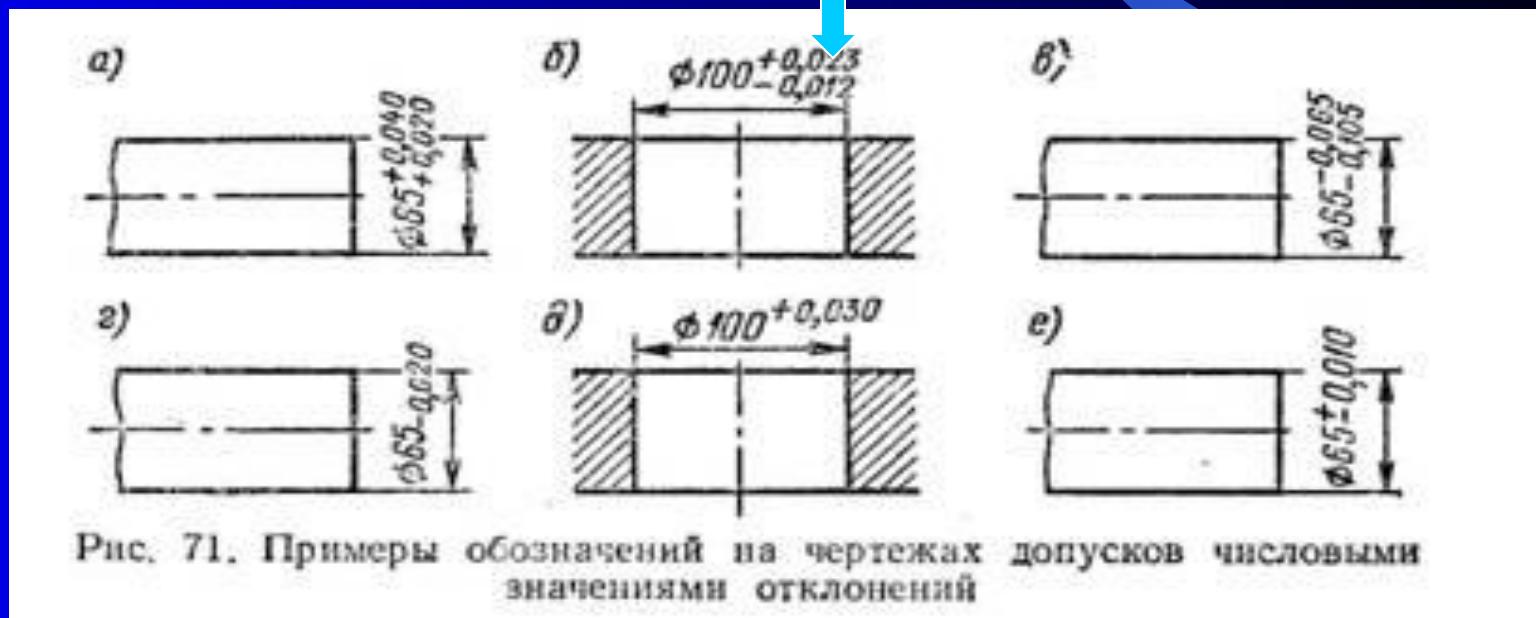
Примеры обозначений на чертежах допусков числовыми значениями отклонений
